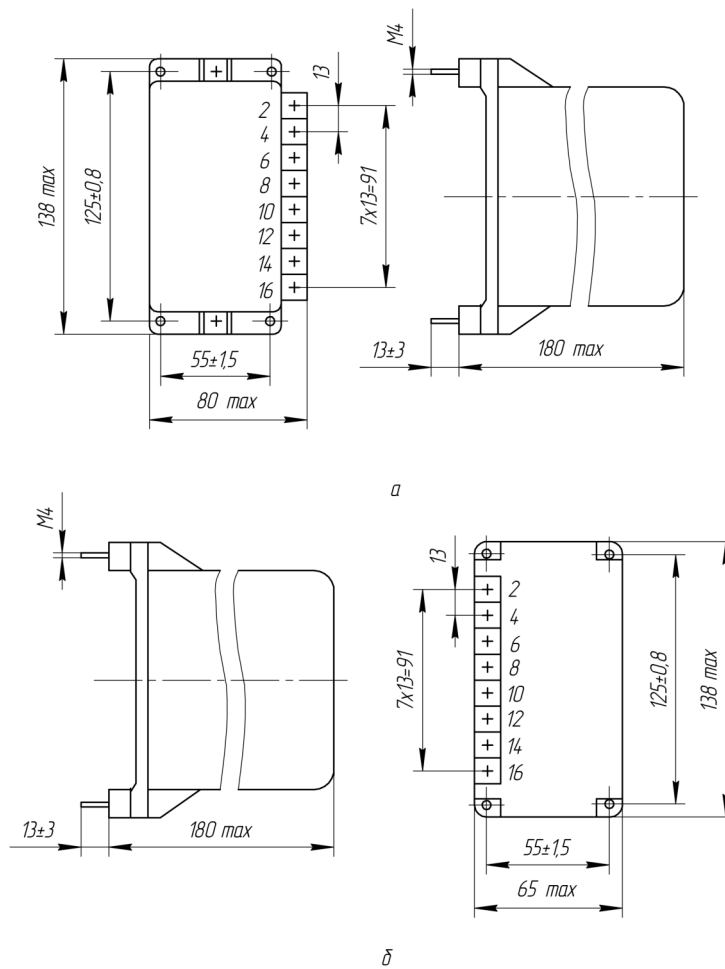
Габаритные, установочные присоединительные размеры вспомогательного устройства ВУ-БЭ1102
